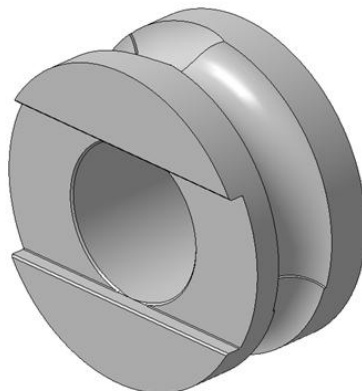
Кольцевой калибр в рабочей клетки “ДУО”
